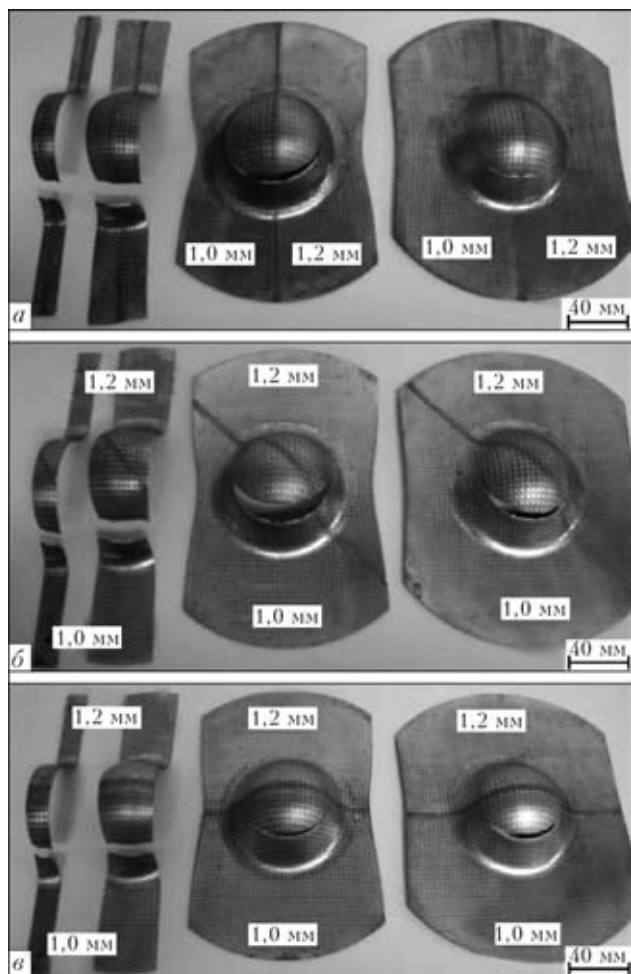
Деформированные элементы из ССЗ (1,0 + 1,2 мм), полученные сваркой в различных направлениях с углами сопряжения: а — 0; б — 45; в — 90°
